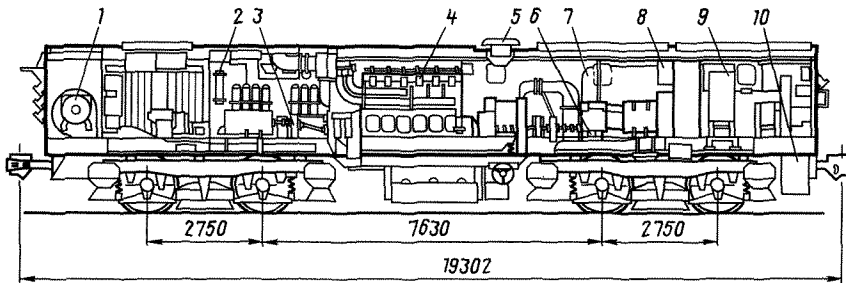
Расположение оборудования на секции автономного питания тягового агрегата ОПЭБ: 1— мотор-вентилятор; 2— топливоподогреватель; 3— раздаточный редуктор; 4— дизель-генератор; 5— вентилятор; 6— компрессор; 7— установка охлаждения главного генератора и выпрямителей; 8— блок выпрямителей; 9— блок силовых аппаратов; 10— резисторы ослабления возбуждения
